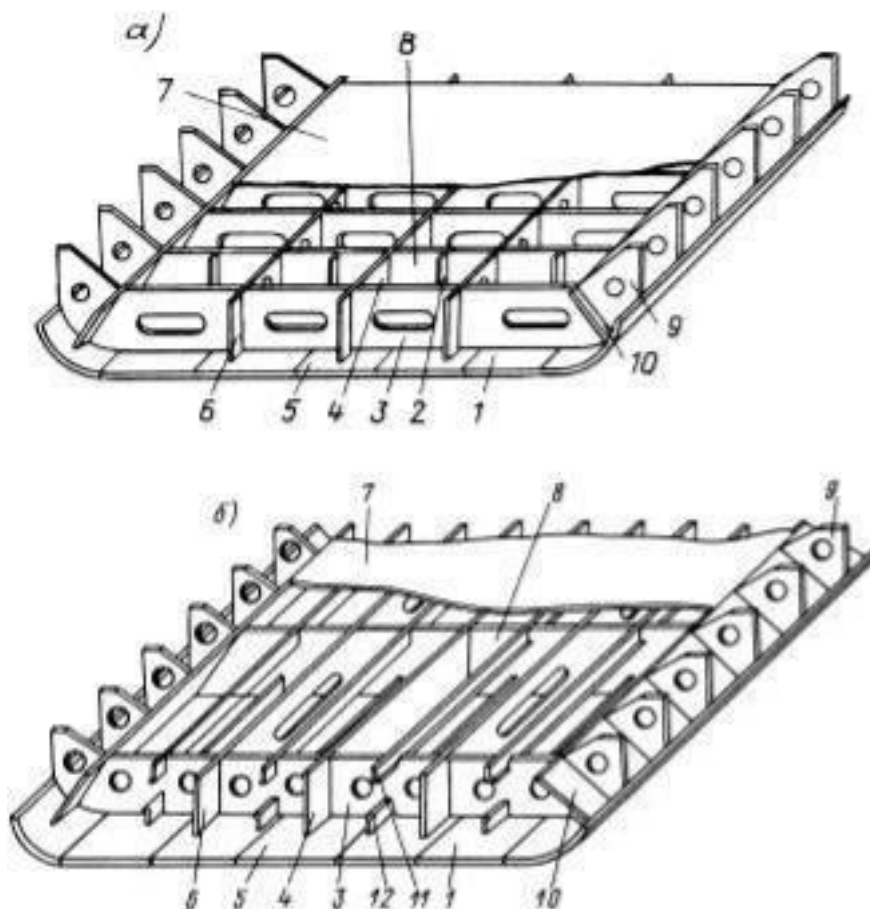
Конструкция днищевого перекрытия с двойным дном:
